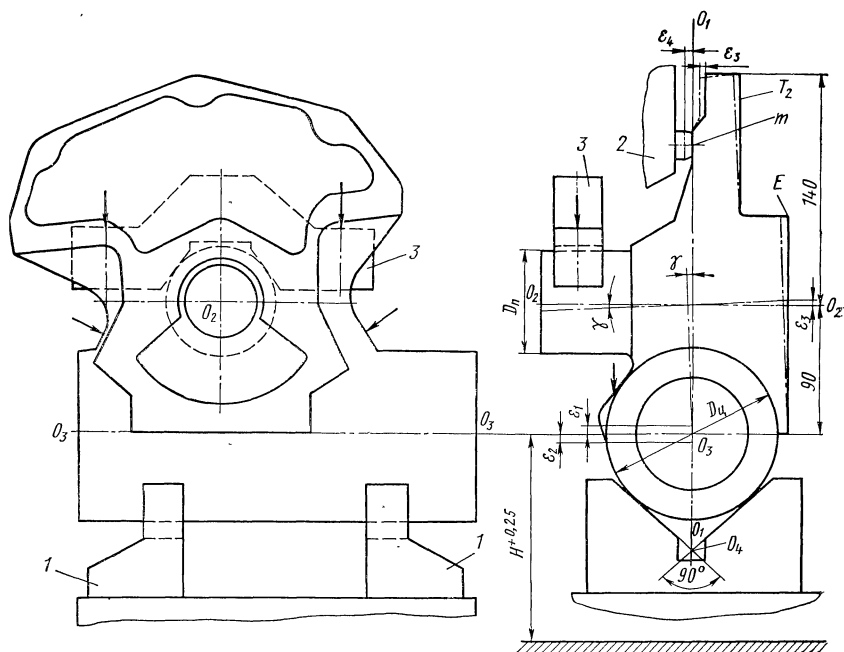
Расчет погрешностей базирования заготовки в спутнике
